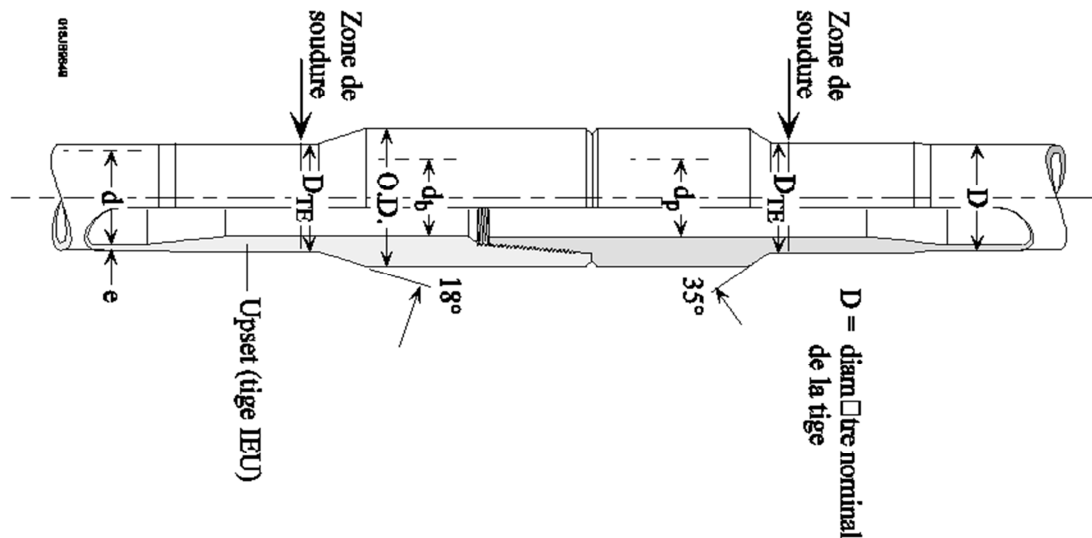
Détail d'une tige (corps et tool-joints)
